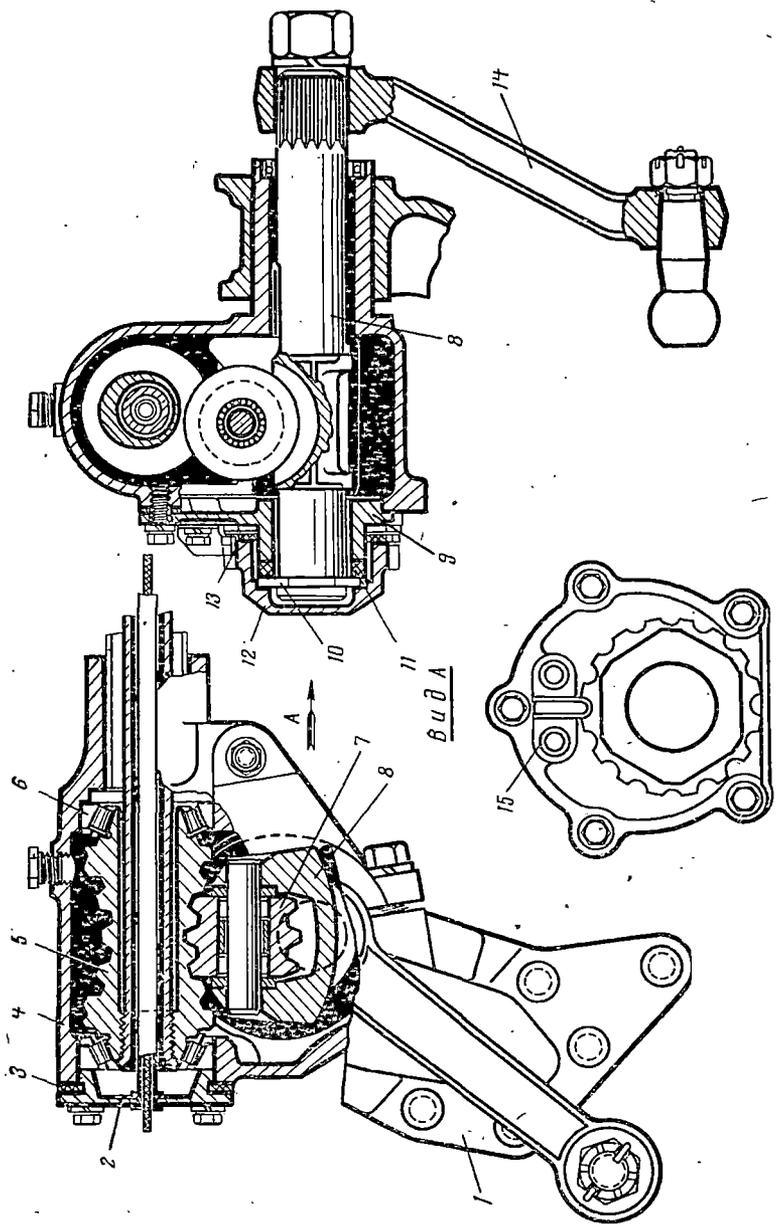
Схема устройства рулевого механизма автомобиля ЗИЛ-164А:
